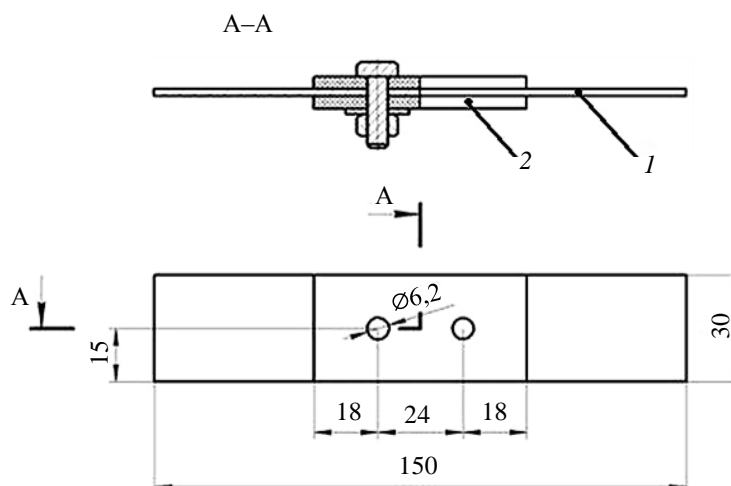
Эскиз конструктивно-подобного образца: 1 – анод (алюминиевый сплав); 2 – катод (углепластик)
